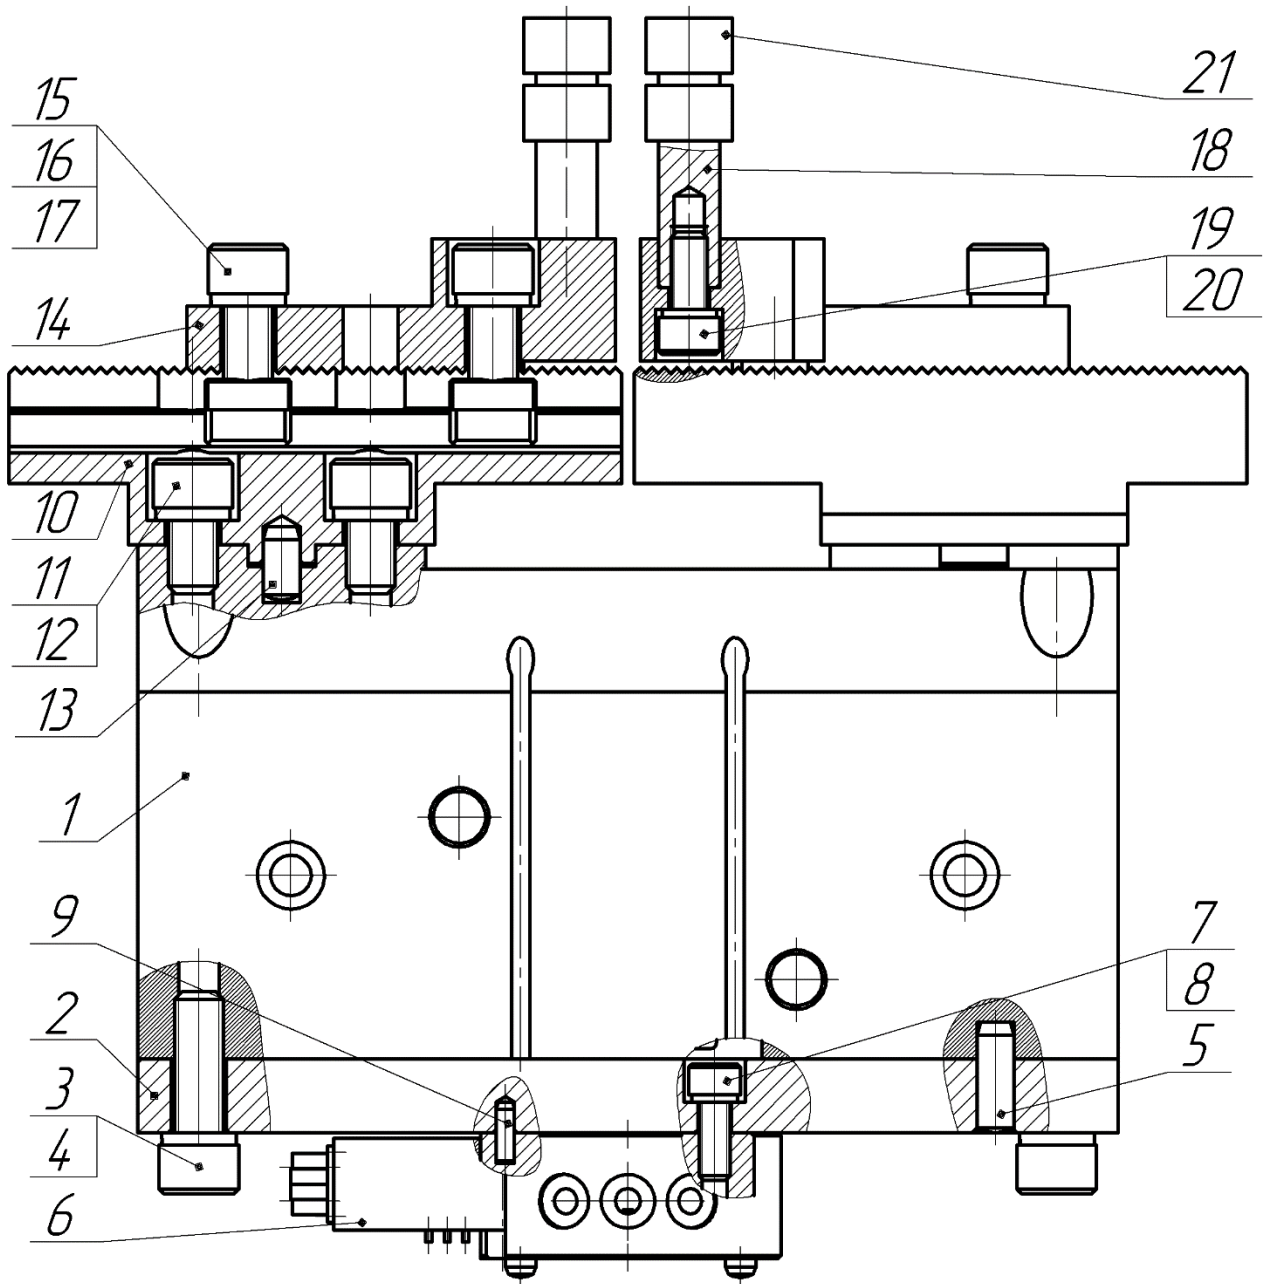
Захоплювальний пристрій для деталей типу шатуни.
